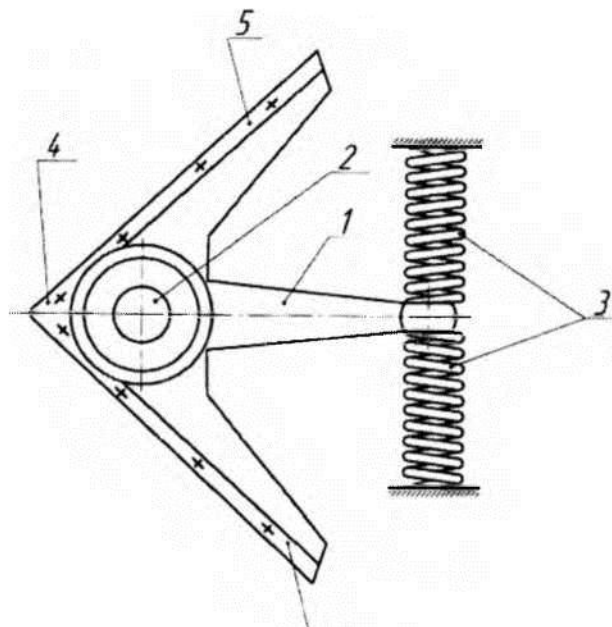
Робочий орган культиватора [15], вид зверху
